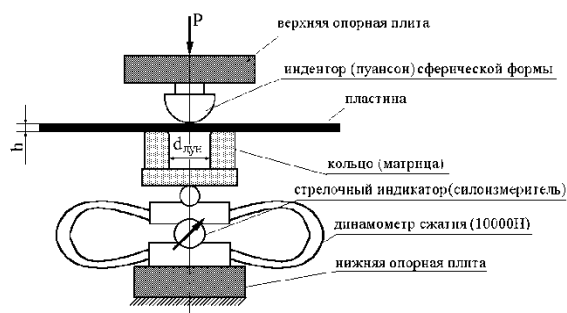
Схема нагрузочного приспособления для образования сферической лунки в стальной пластине
